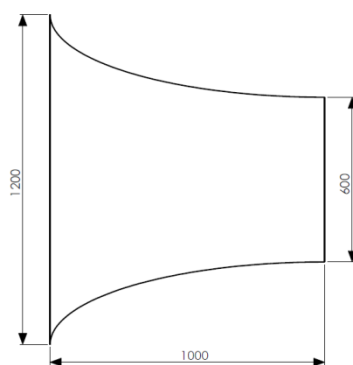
Geometria e dimensões do elemento de admissão do túnel.
